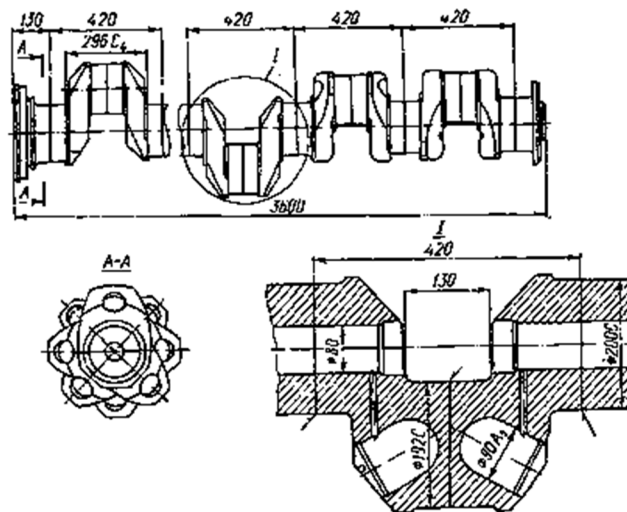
Сварной коленчатый вал дизеля
